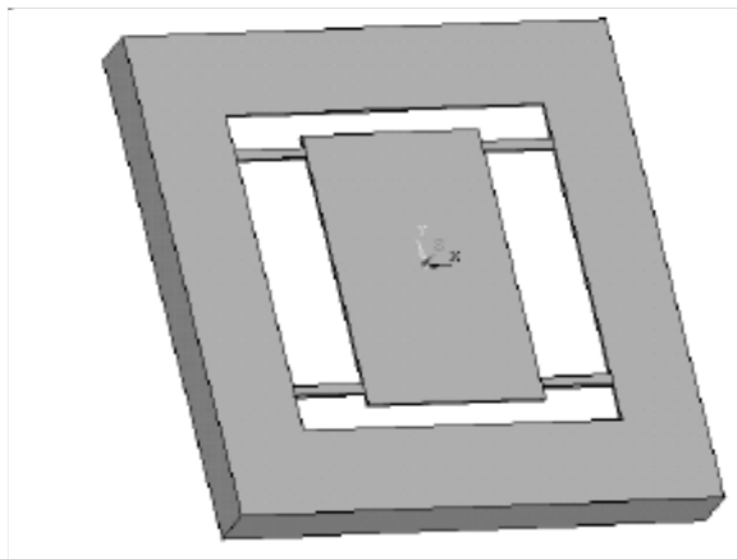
Estructura tradicional de vigas bilaterales adaptado de (10)
